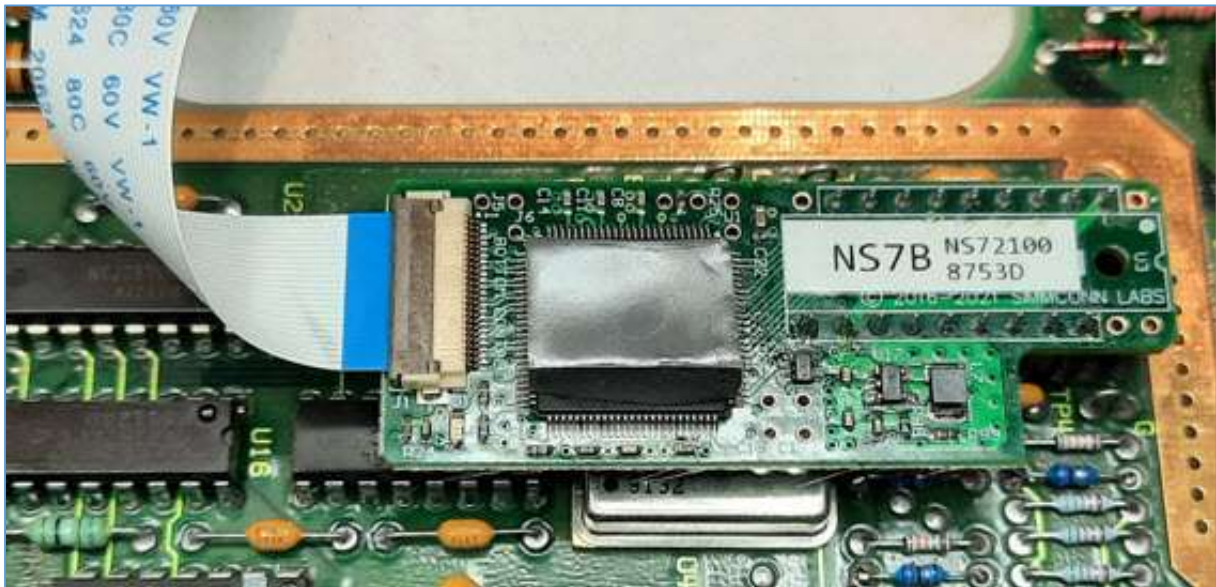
Placement d'un thermal pad sur le circuit intégré SMD de l'interface Photo : ON4IJ.
